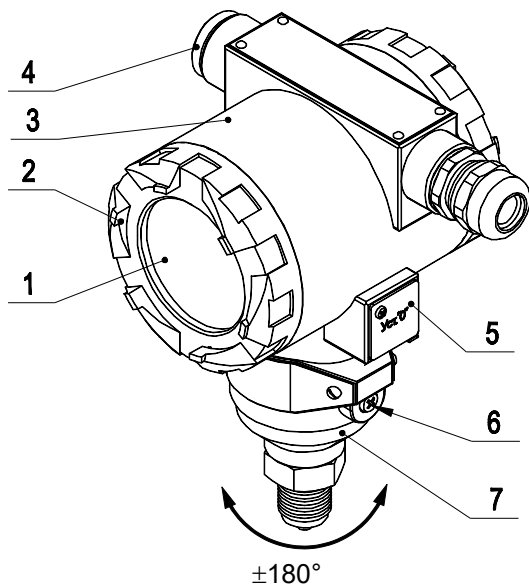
Общий вид AIR-30M (корпус АГ-30)
